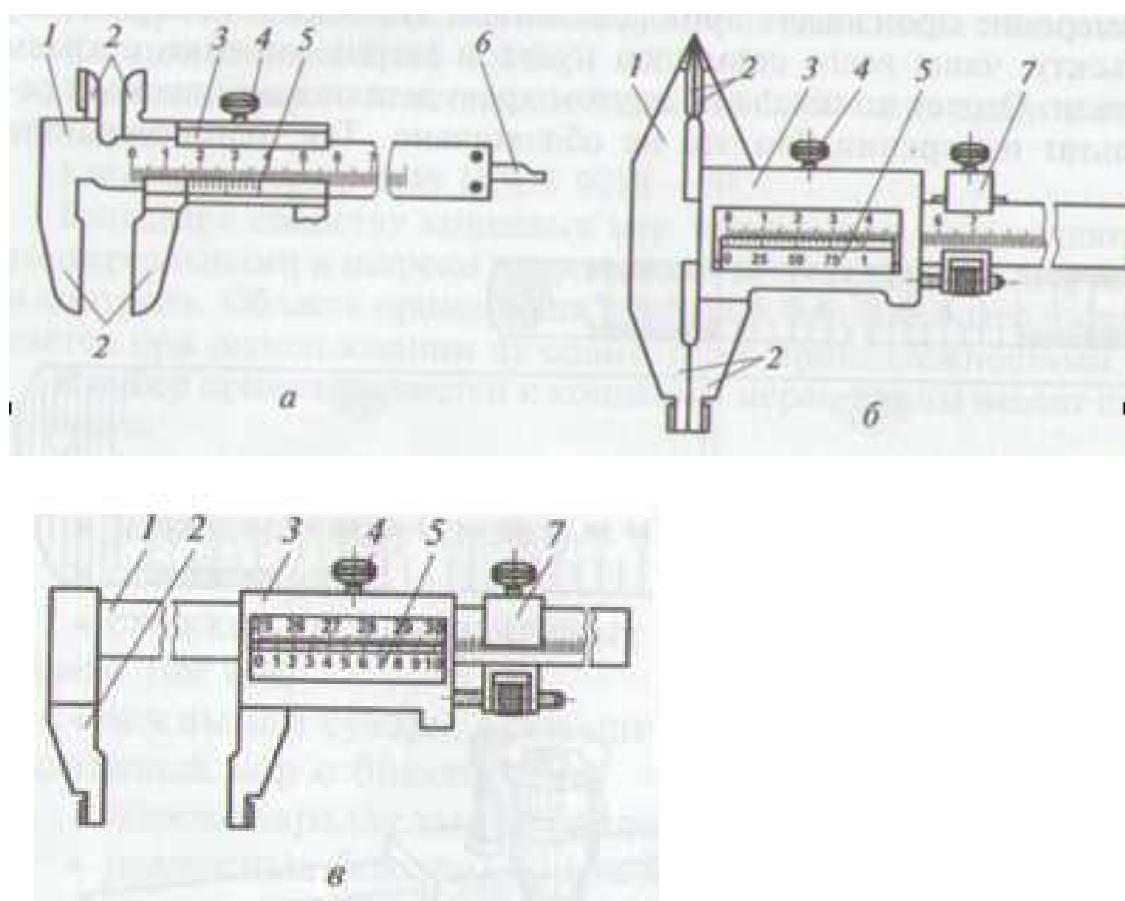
Штангенциркули типа: а – ШЦ-1; б – ШЦ-2; в – ШЦ-3
